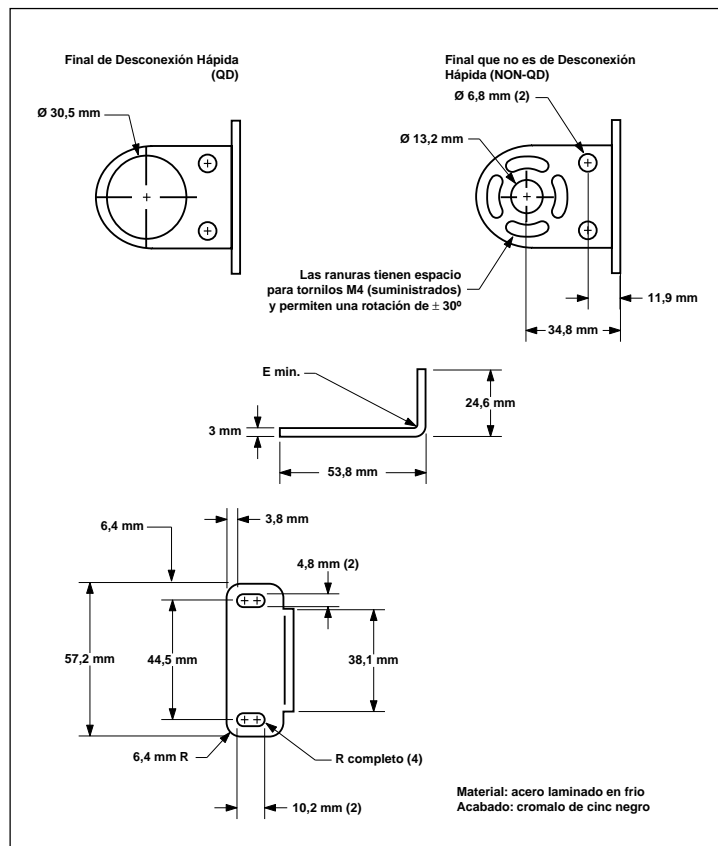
Dimensiones de Ménsula de Montaje de Emisor y Receptor
